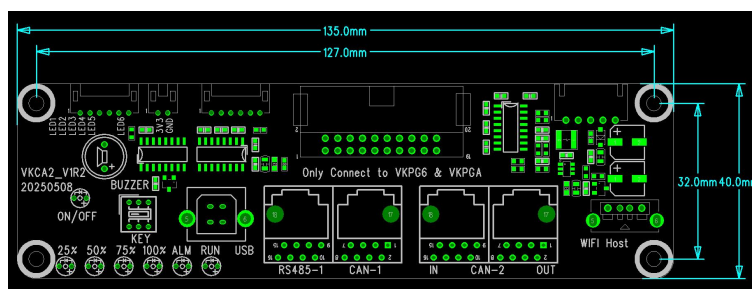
分体端子板尺寸图 Fig. 10-6 Dimension Diagram of the Split Board Board
